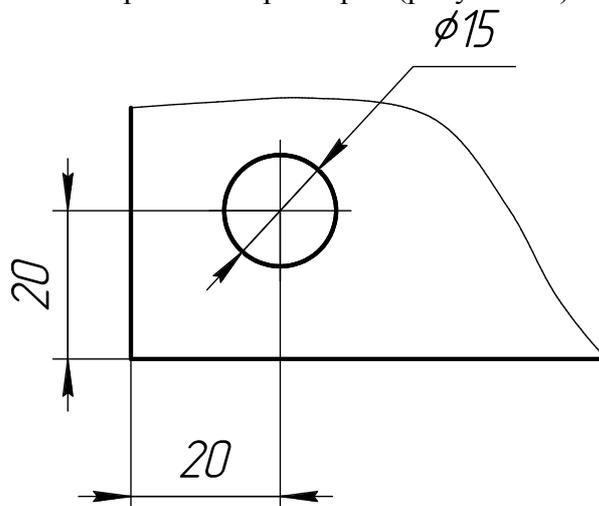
Нанесение размеров на расположение отверстий на детали
